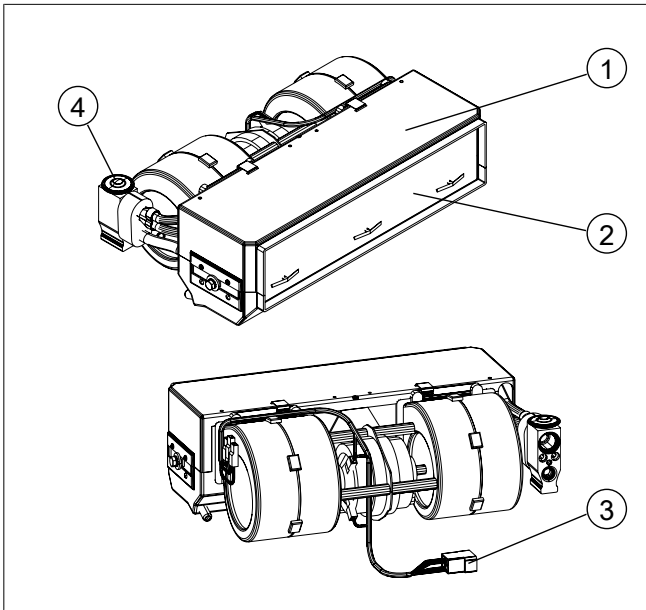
Vue d'ensemble de l'Oakland R1234yf
